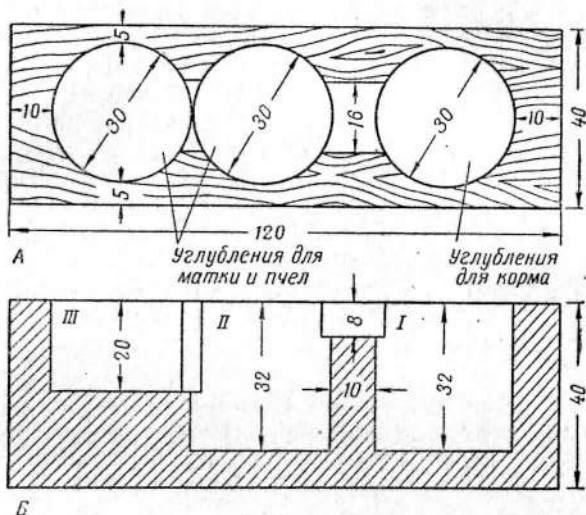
Клеточка для почтовой пересылки маток: А — вид сверху, Б — боковой разрез (размеры указаны в миллиметрах).
